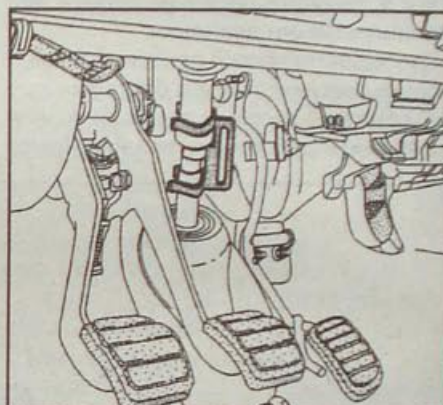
Установка приспособления Dir. 1408 для регулировки положения вилки карданного шарнира рулевого вала относительно приводной шестерни рулевой передачи
